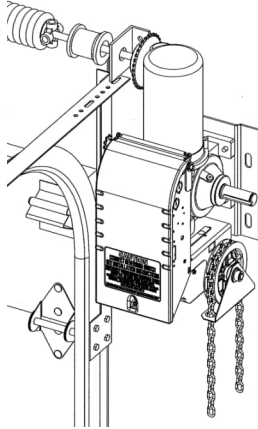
Montaje de pared lado derecho con BRACKET112 (polea de cadena a la derecha)
